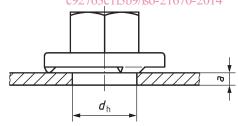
Dimensions de raccordement (écrou non soudé au-dessus)
